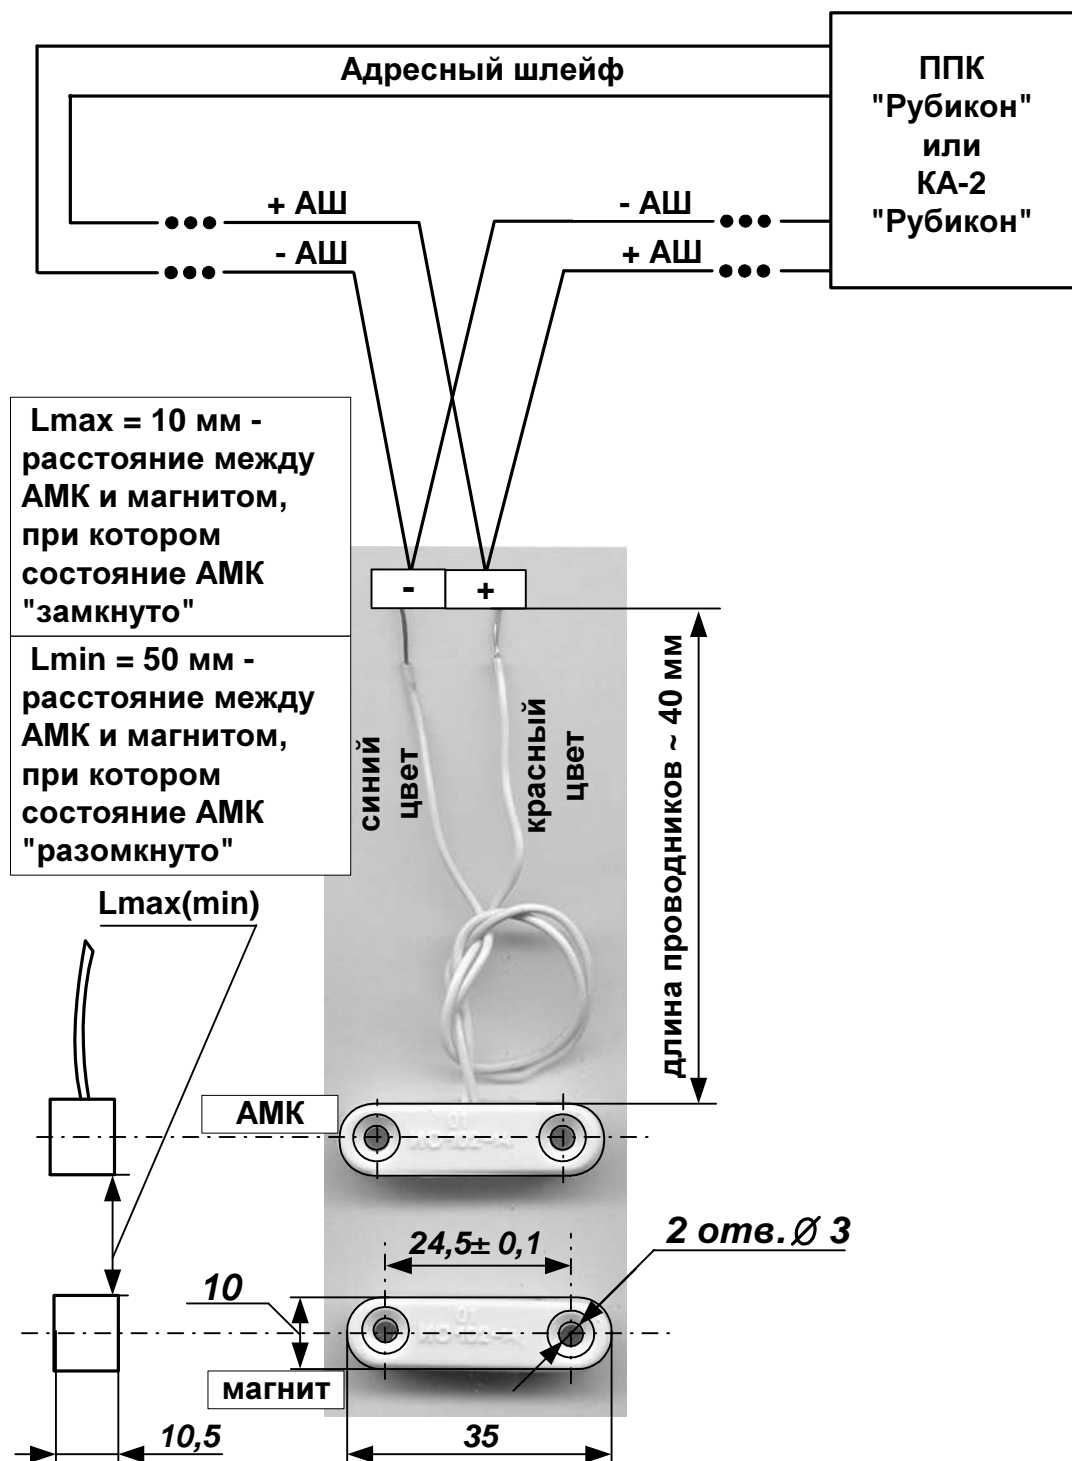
Конструкция, подключение, габаритные и присоединительные размеры
